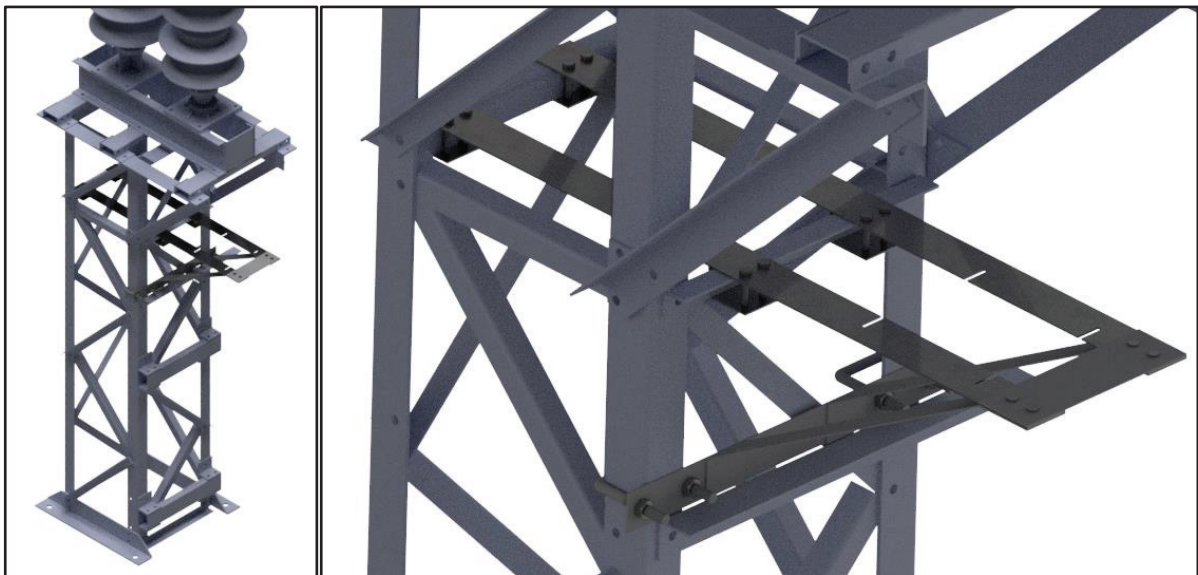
Montagem final do suporte do motovibrador da chave seccionadora BMKU-40A
